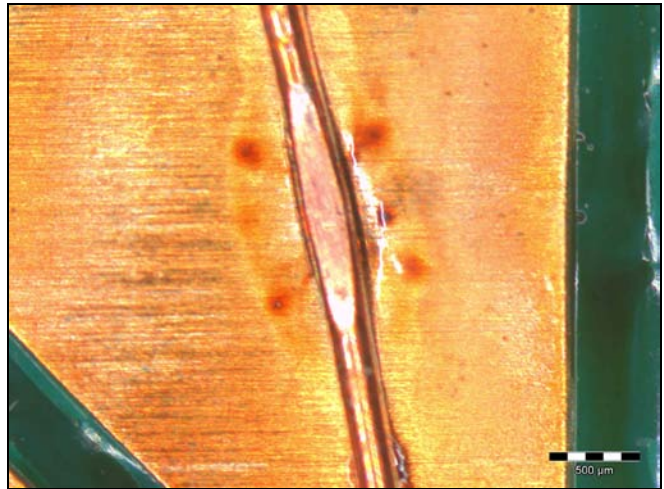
Anwendung Elektronik – Geschweißter Kupfer-Lackdraht Durchmesser 50µm.
